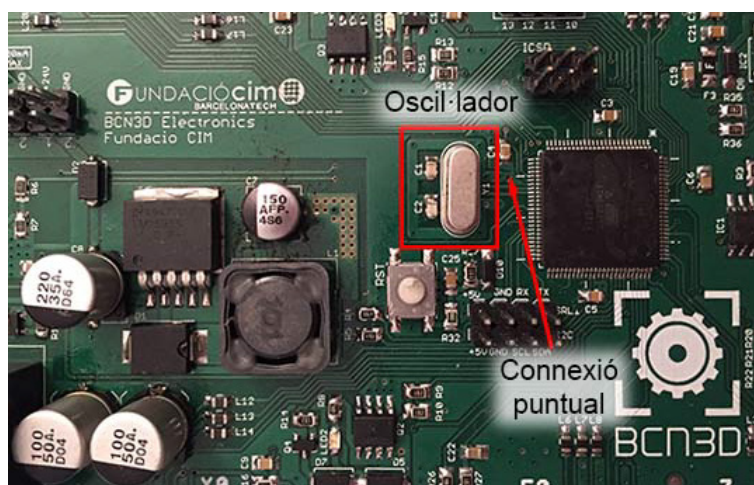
Component oscil·lador de la PCB, amb el punt únic de connexió indicat.
